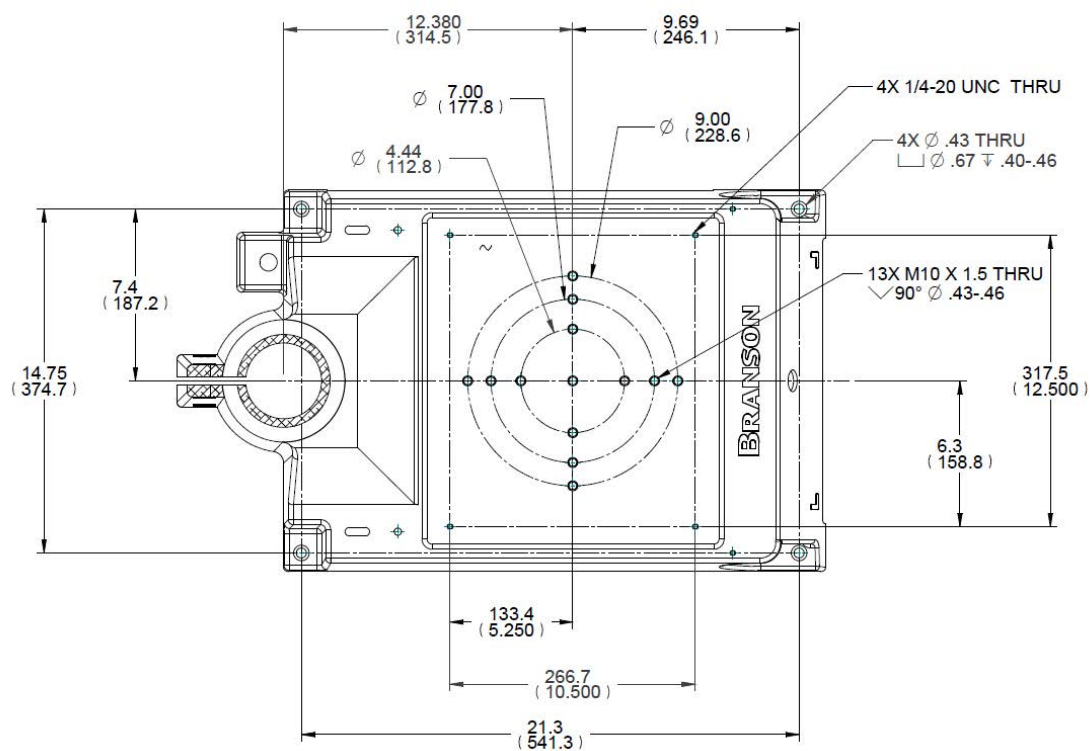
Parte izquierdaFigura 3.4 Parte derecha
